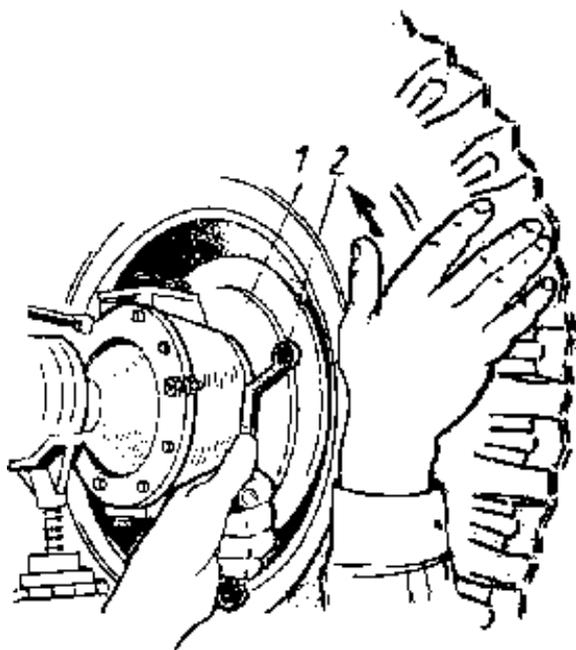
Регулировка зазора между колодкой и тормозным барабаном:
